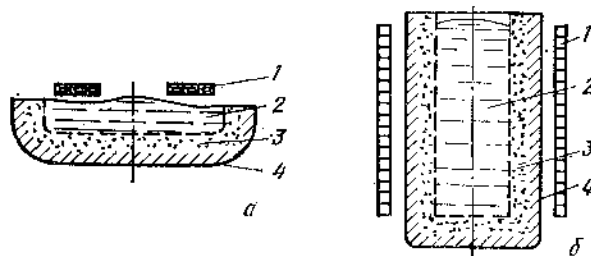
Схемы индукционной гарниссажной плавки: а — нагрев сверху; б — нагрев сбоку; 1 — индуктор; 2 — расплав; 3 — гарниссаж; 4 — охлаждаемая поверхность
